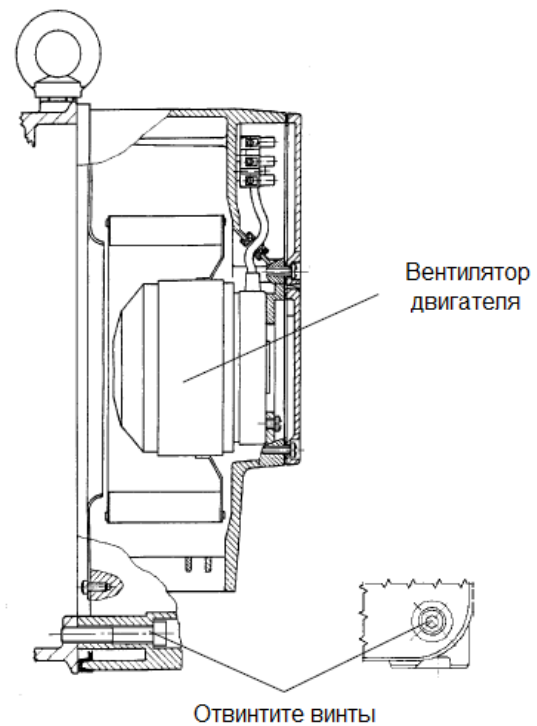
Демонтаж / монтаж вентилятора двигателя
